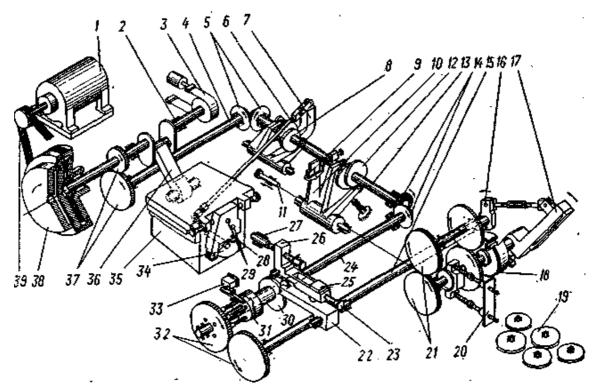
Кинематическая схема холодновысадочного двухударного автомата
